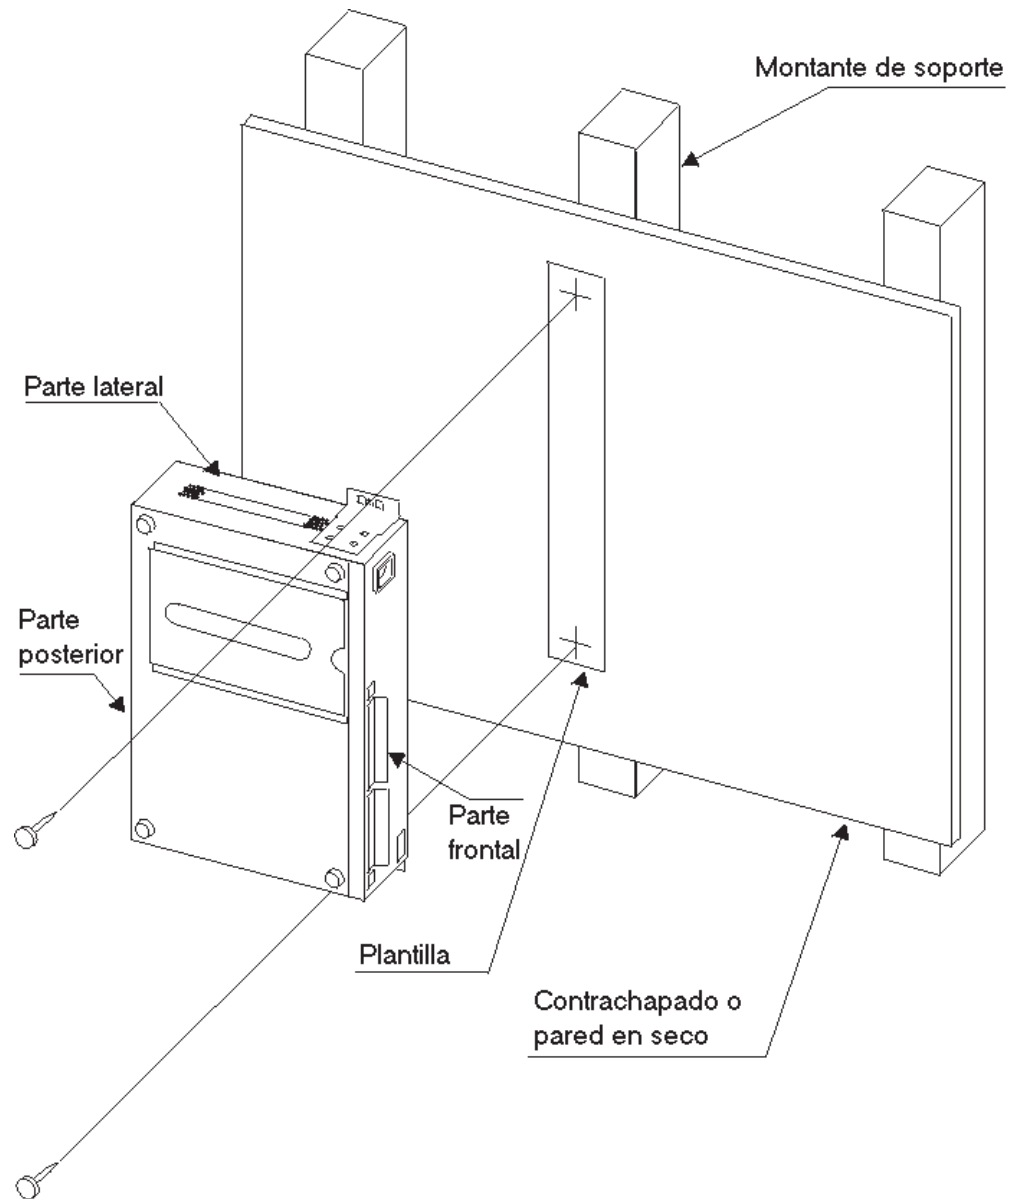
Montaje del Conmutador de sobremesa Fast Ethernet 8275-324 en la pared
